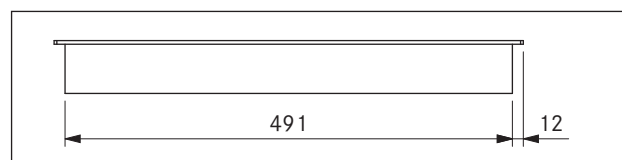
Dimensões do aparelho CKI, vista lateral
